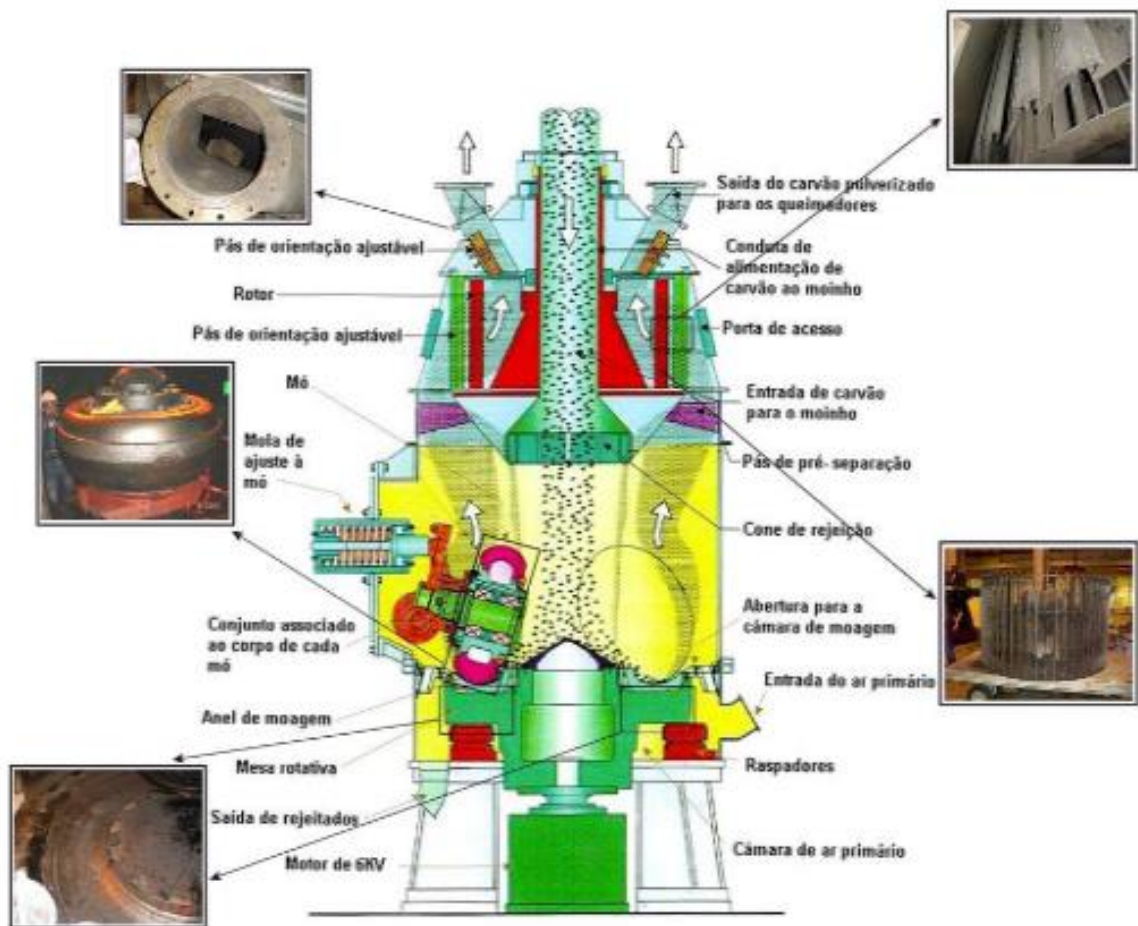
Componentes de um moinho a carvão e o processo de moagem [11].
